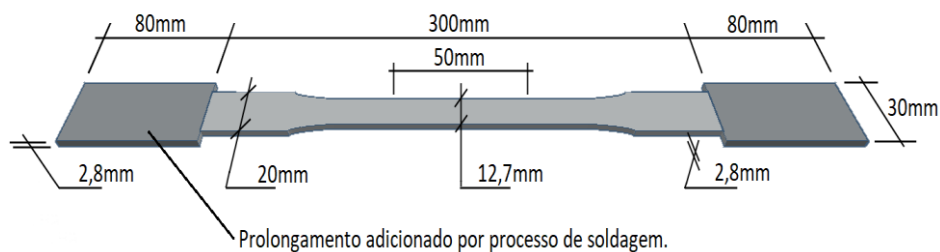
Geometria e dimensional dos corpos de prova de tração utilizados
